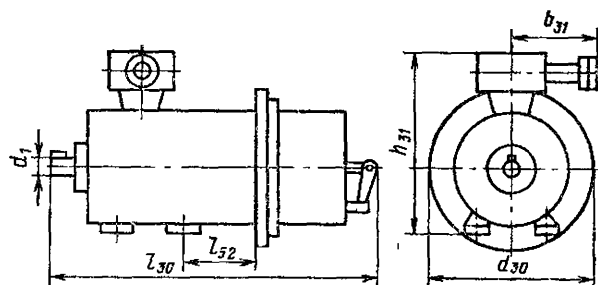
Основные размеры двигателей серии ВКр исполнения М101.
